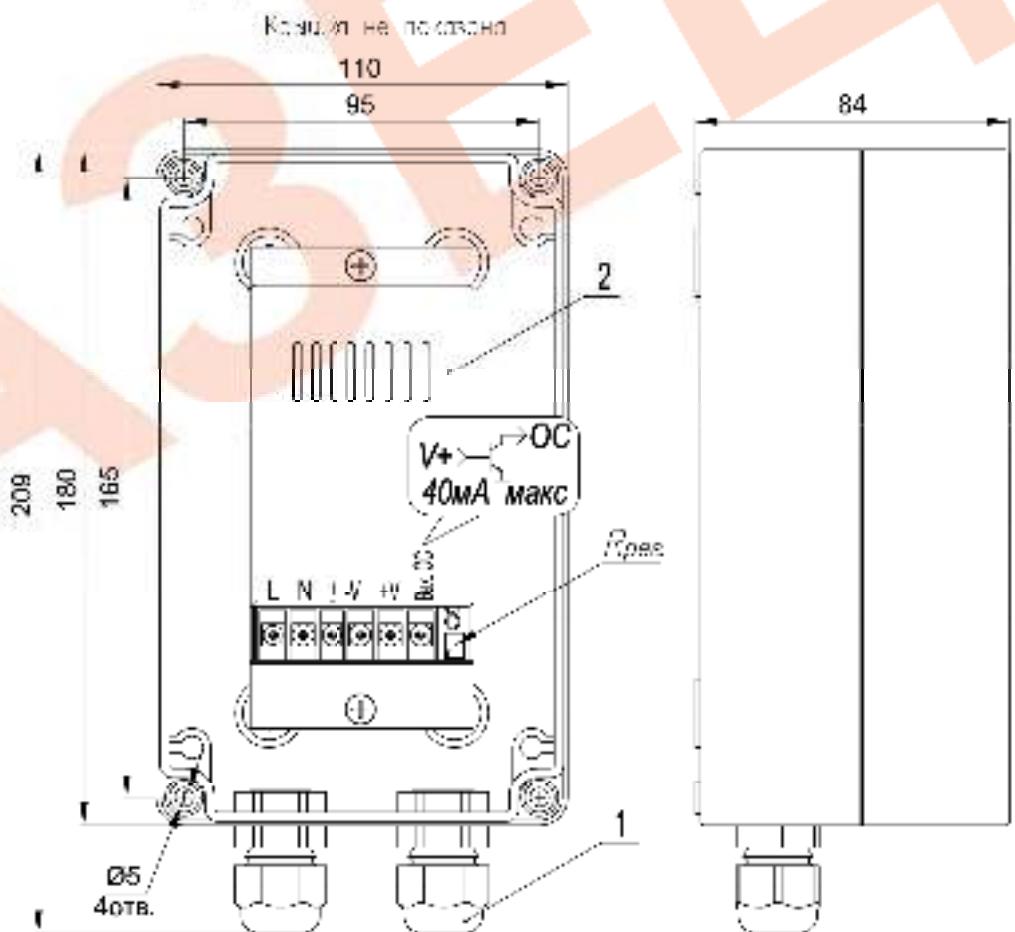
Устройство, габаритные и установочные размеры БПГ-36Вт.
